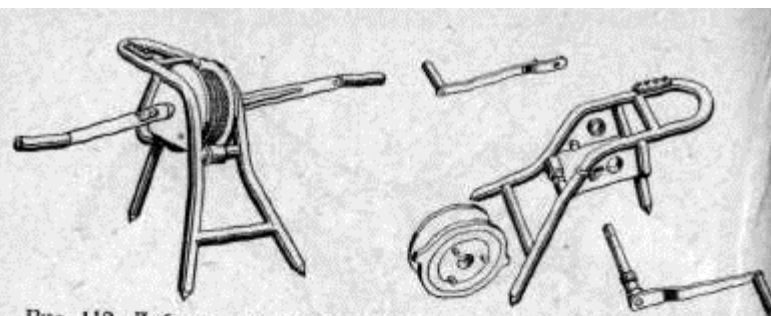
Лебедка для подъема и спуска пострадавшего (общий вид и детали)
